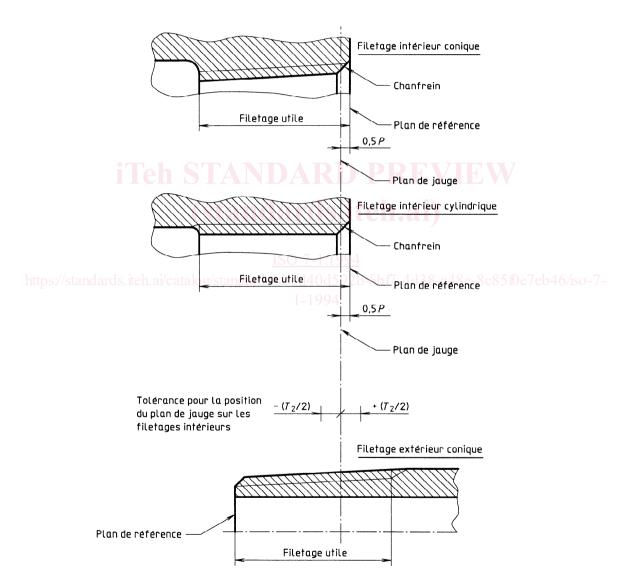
Filetages intérieur et extérieur de tuyauterie (position du plan de jauge, plan de référence, filetage utile)
